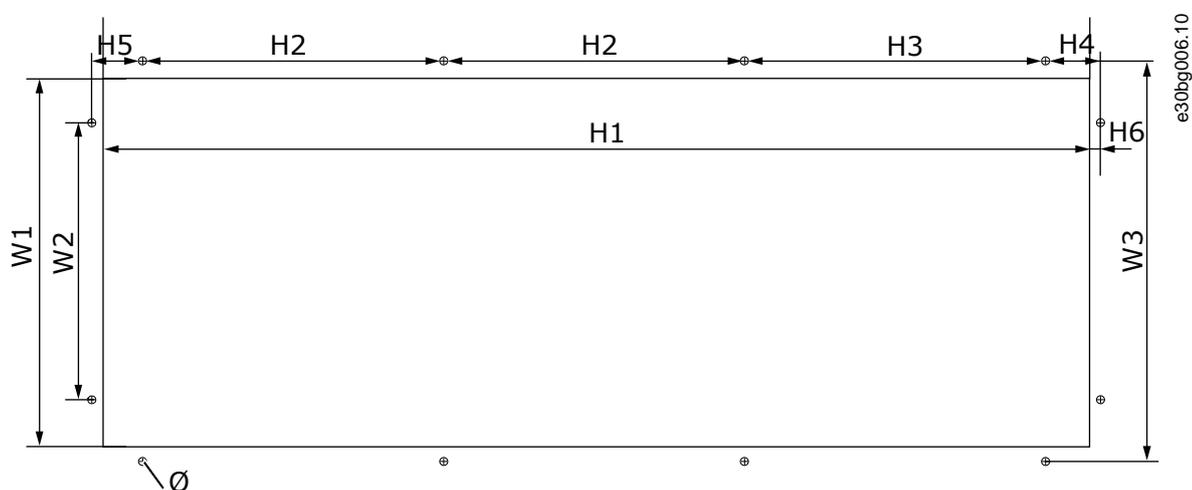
Dimensões da abertura e contorno do conversor com flange, FR7
